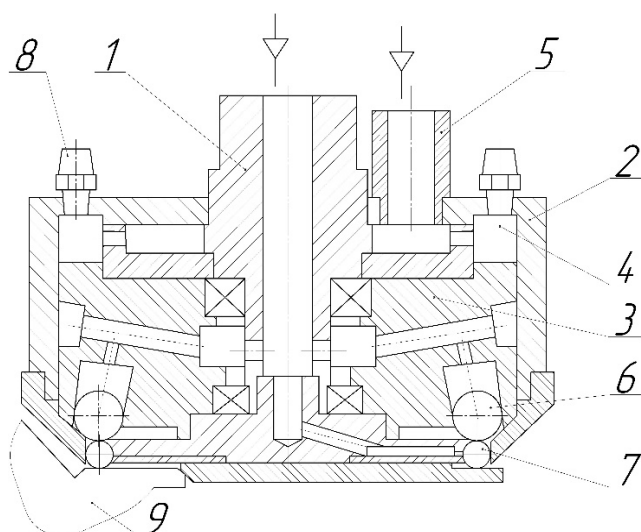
Конструкция инструмента для упрочняющей обработки пневмоударом плоских поверхностей: 1 – полый вал; 2 – корпус; 3 – диск; 4 – лопатки; 5 – штуцер; 6 – приводящие шары; 7 – деформирующие шары; 8 – пневмоглушители; 9 – заготовка
